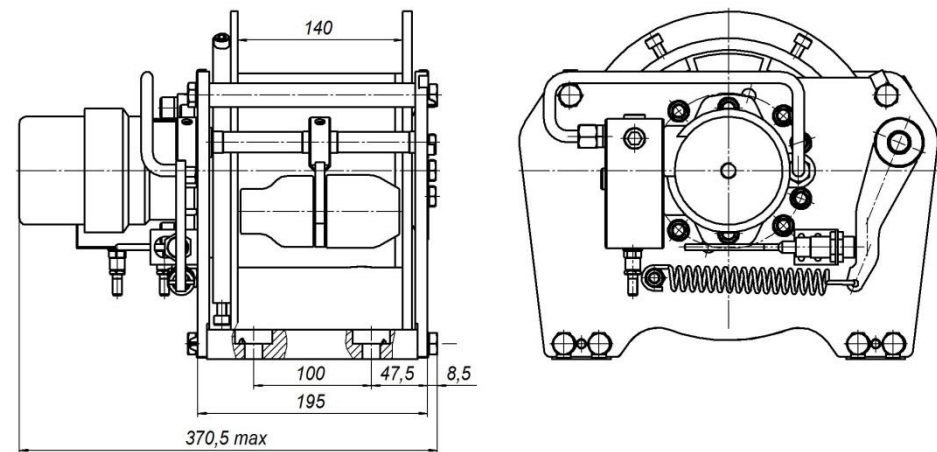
Общий вид, габаритные и присоединительные размеры
